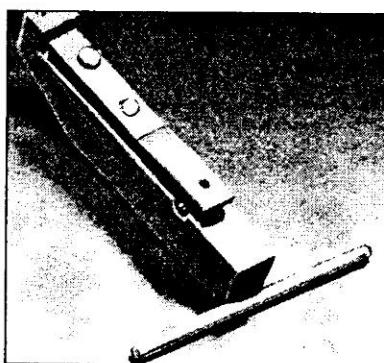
Кондуктор для сверления отверстий в цилиндрической детали
